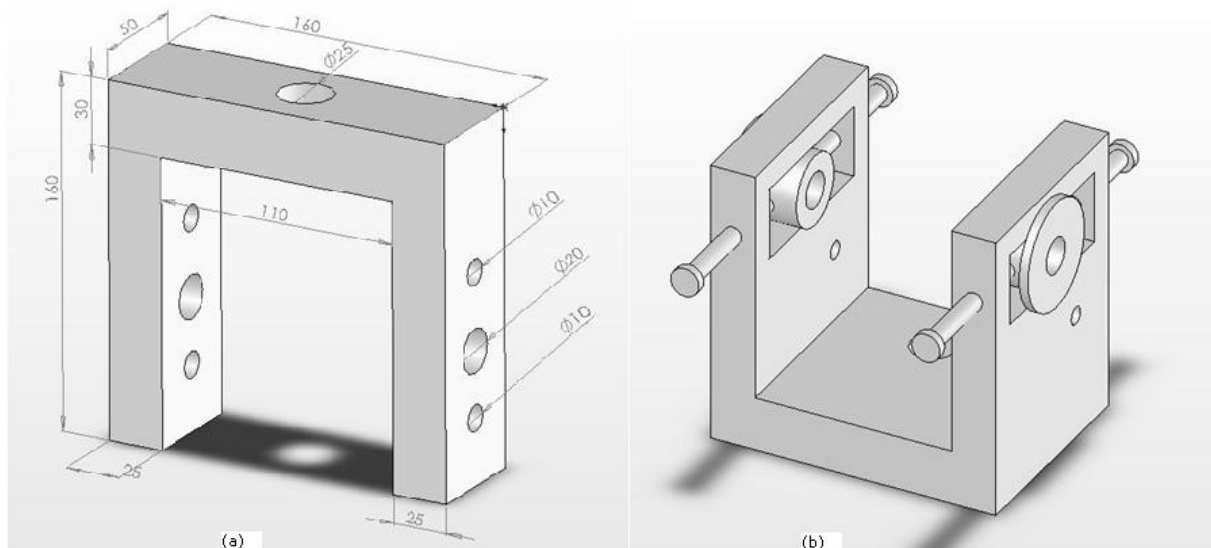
Apoios da suspensão e amortecedor projectados: (a) apoio superior; (b) apoio inferior.
